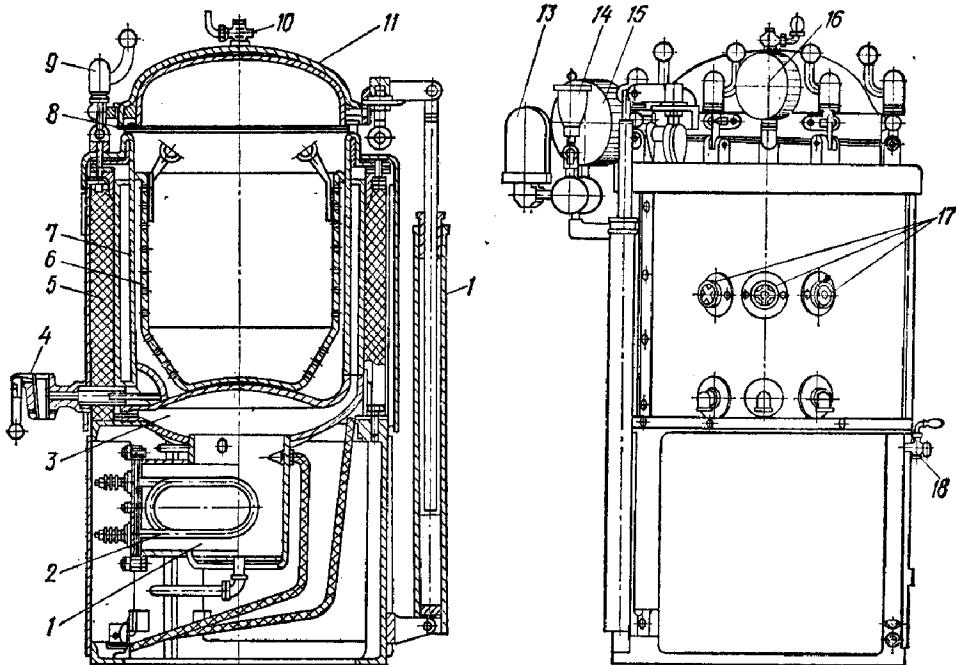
Автоклав АЭ-1: 1 – парогенератор; 2 – нагрівальний елемент (ТЕН); 3 – пароводяна рубашка; 4 – кран зливний; 5 – теплоізоляція; 6 – сітка завантажувальна; 7 – варильна судина; 8 – резинова прокладка; 9 – відкидний болт; 10 – кран для спуска пари; 11 – кришка; 12 – проти вантаж; 13 – подвійний запобіжний клапан; 14 – заливна воронка; 15 – електроконтактний манометр; 16 – мановакуумметр; 17 – вентилі; 19 – кран рівня
